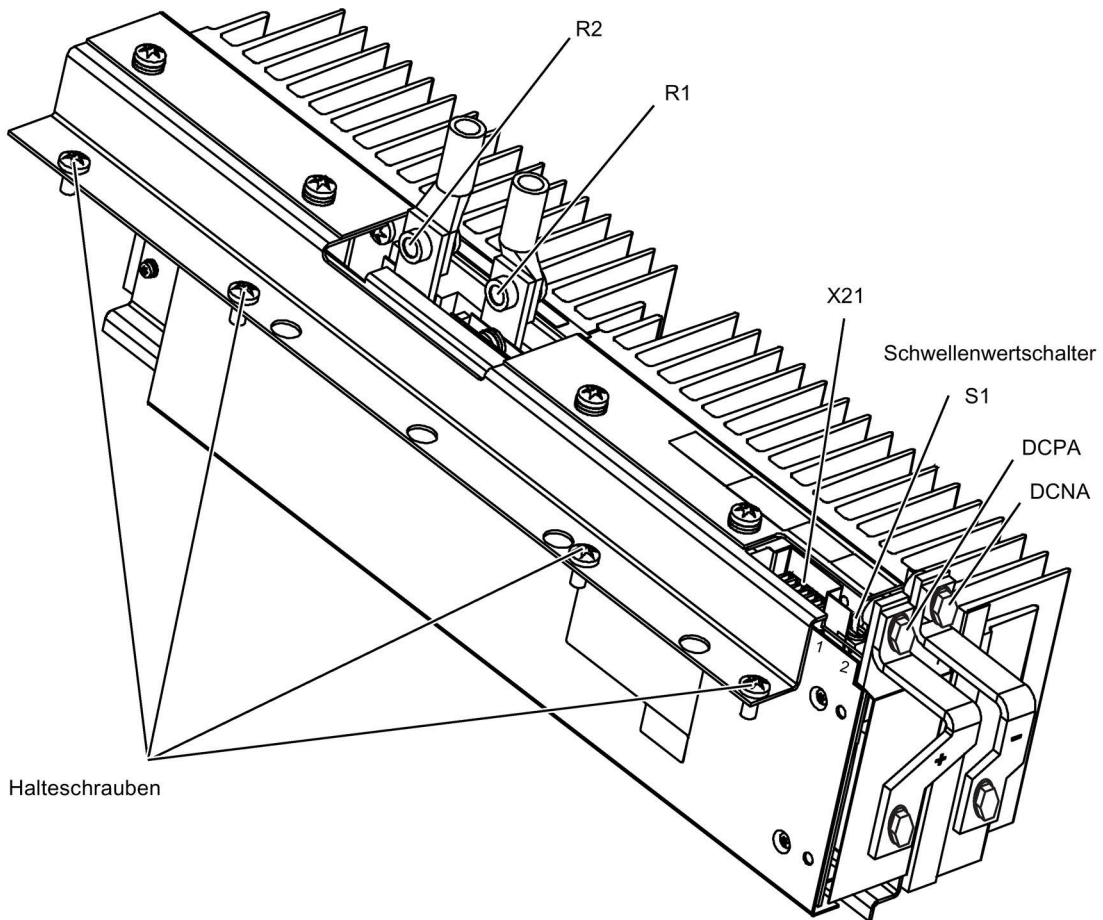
Braking Module für Power Module Baugröße HX / JX
